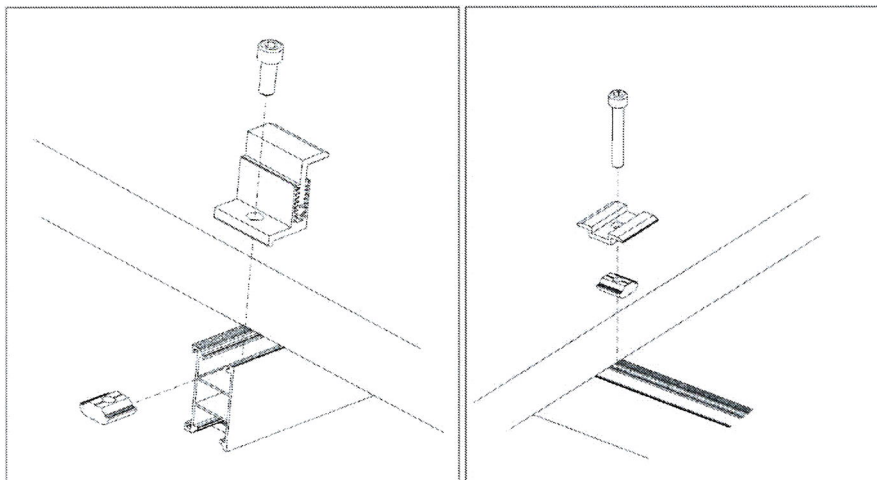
Sposób montażu konstrukcji wsporczej na dachu krytym blachą.
